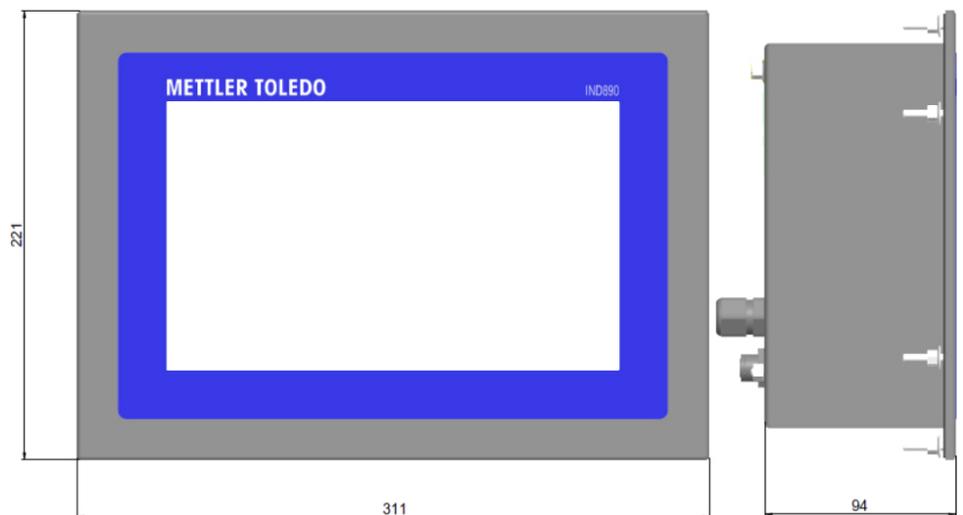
Dimensiones de IND930 para el montaje en cuadro de control
